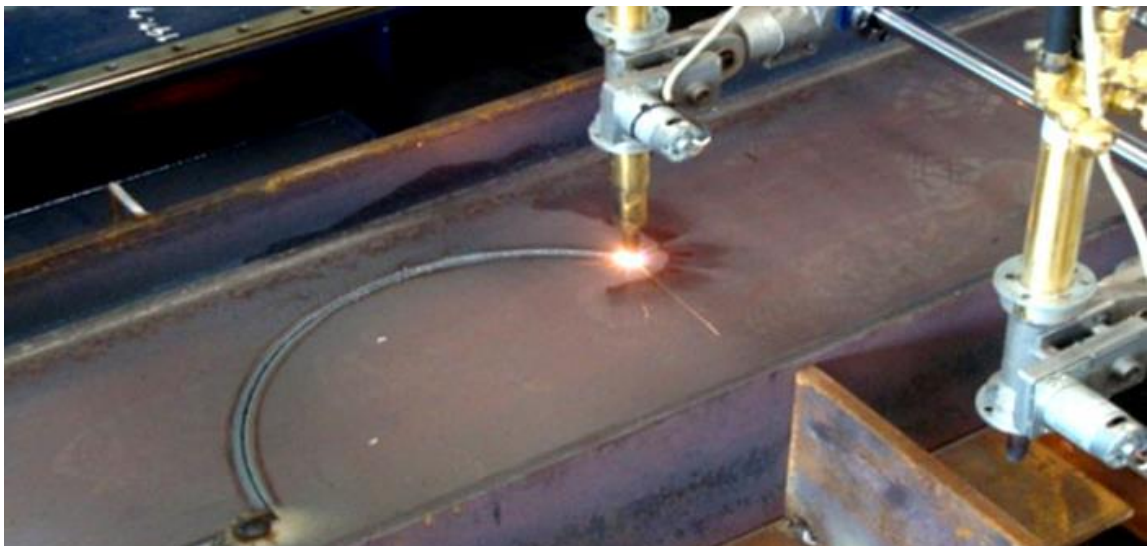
Fabricação de vigas celulares – primeiro corte (fonte: www.kloeknermetalsuk.com, 2016)
